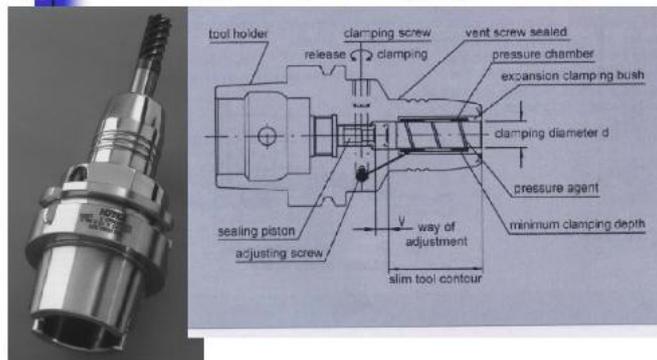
、高速加工刀把與切削刀具夾持方式 4/5[11]
